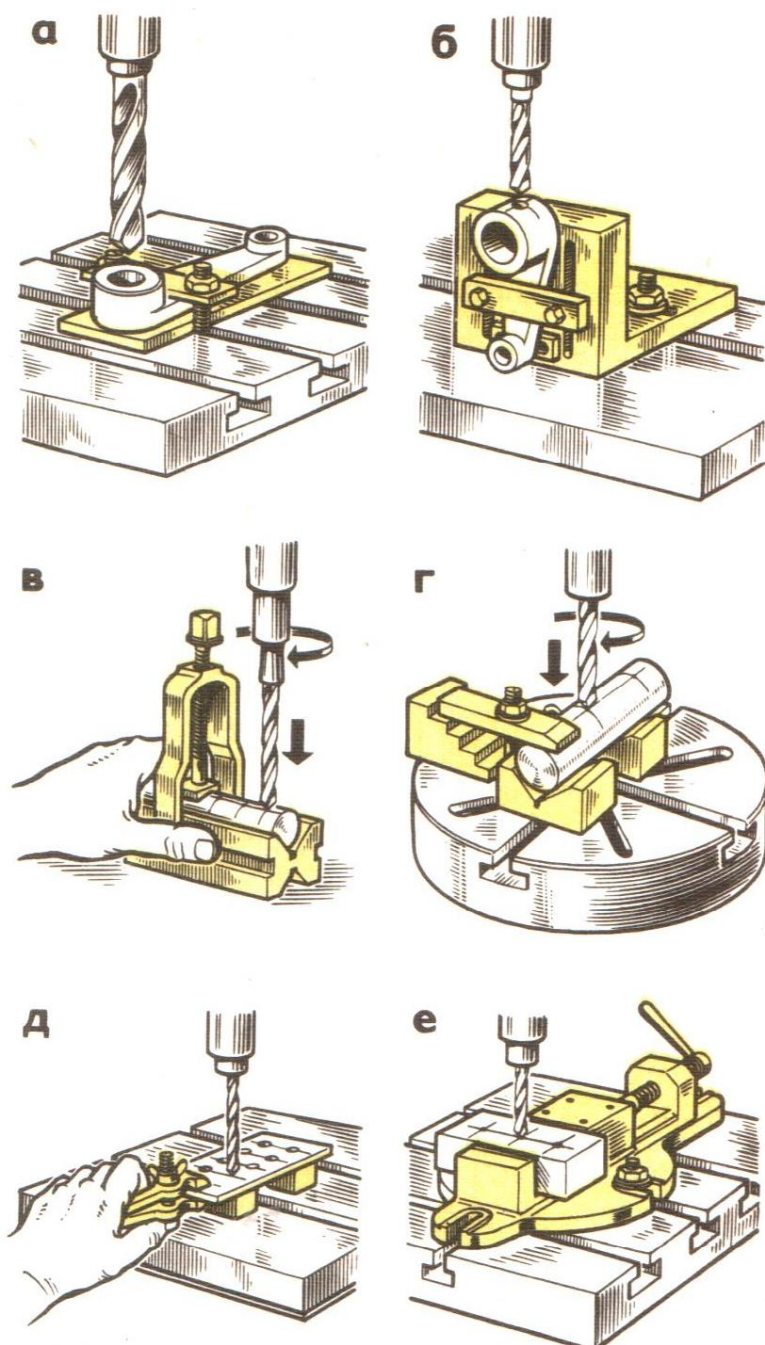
Крепление заготовок при сверлении: а – непосредственно на столе планками; б – на угольнике планками; в – на
